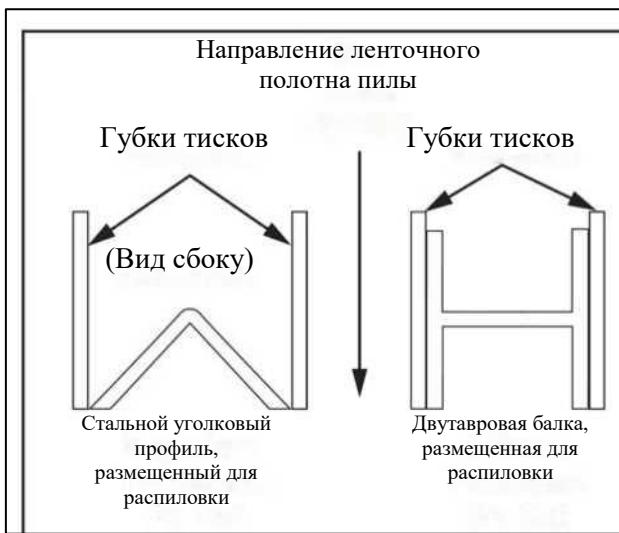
Структурные заготовки, закрепленные в тисках для распиловки.
